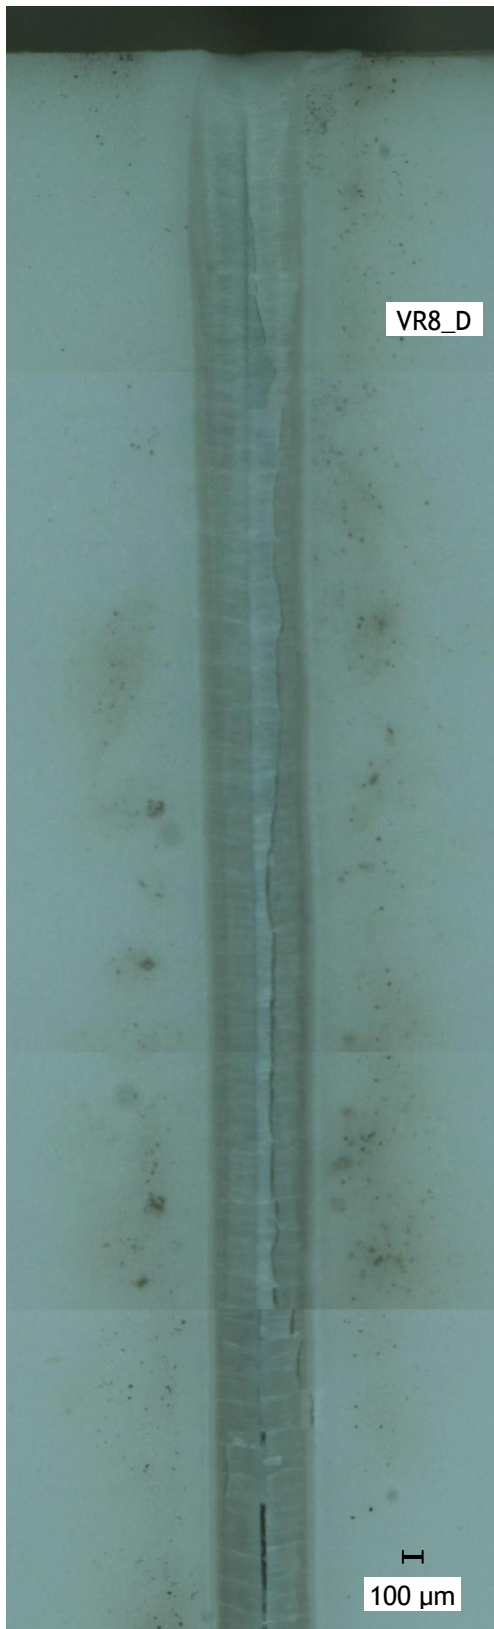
zeigt die Schweißnaht VR8_D von oben, die bei einer Defokussierung von fünf Millimetern erzeugt wurde.
